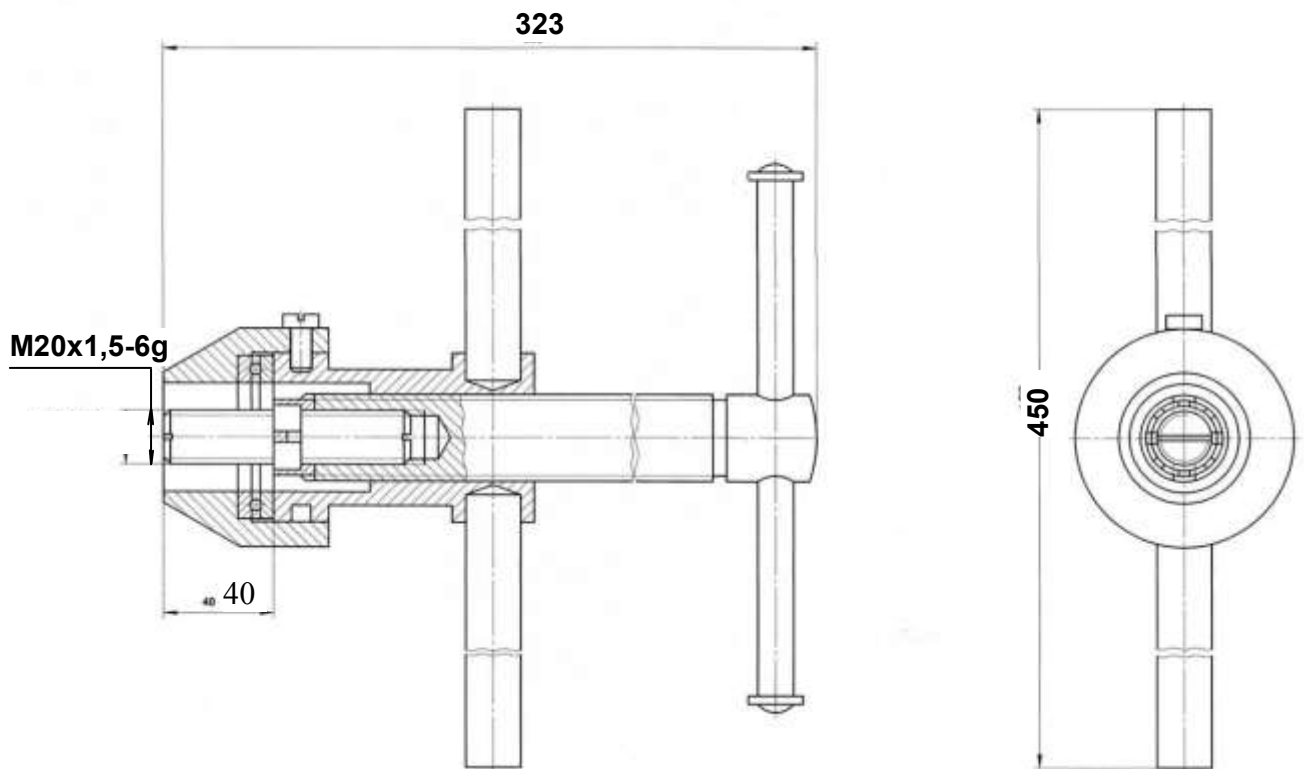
ЗМ 7823-4291-04 Приспособление для напрессовки шкива на коленчатый вал
